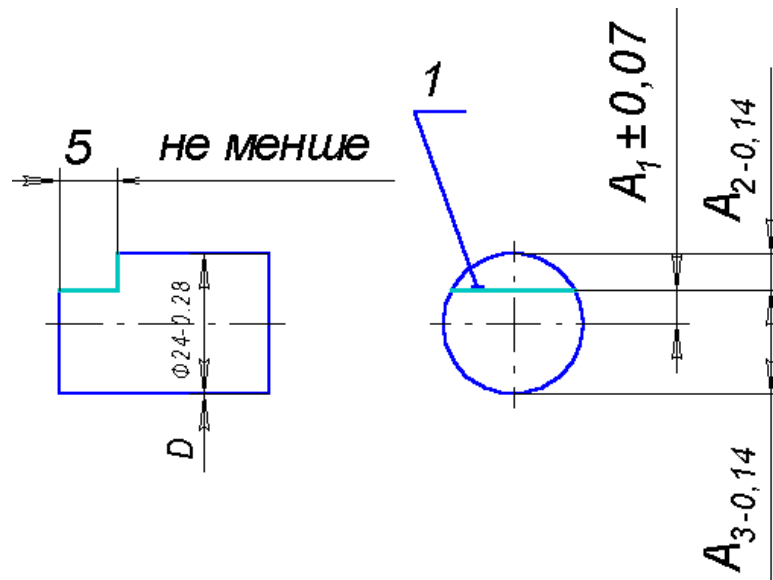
Операційний ескіз оброблюваної заготовки
